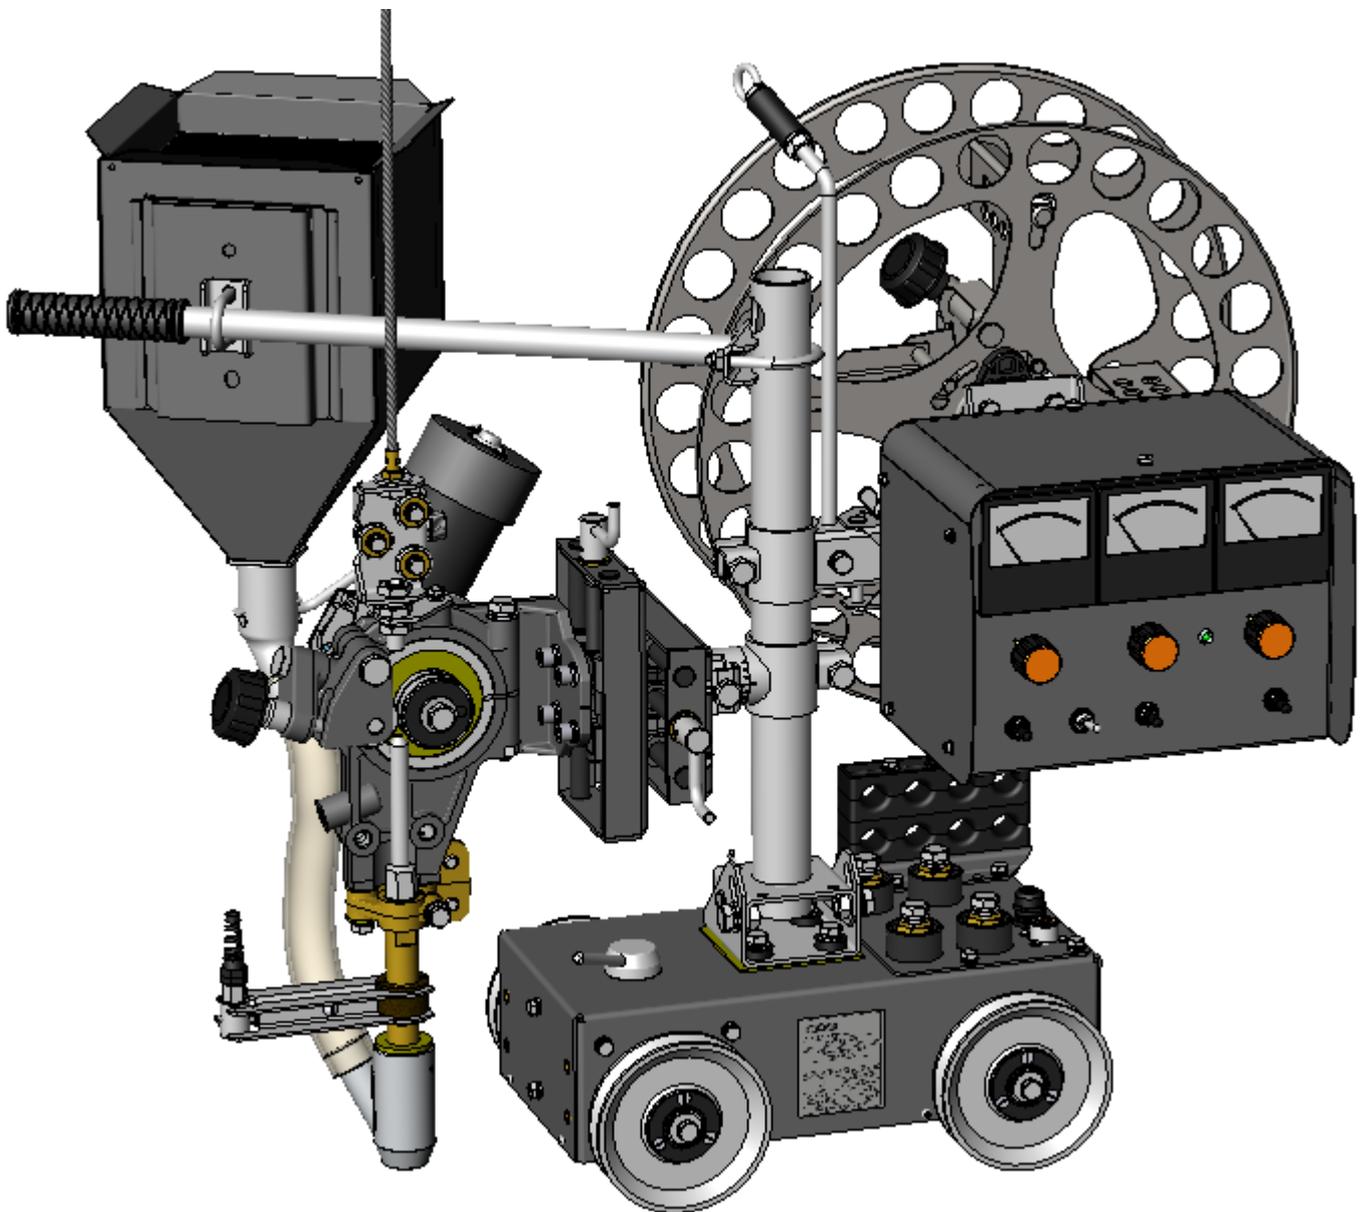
Автомат сварочный АДГ-630 исп.-05
